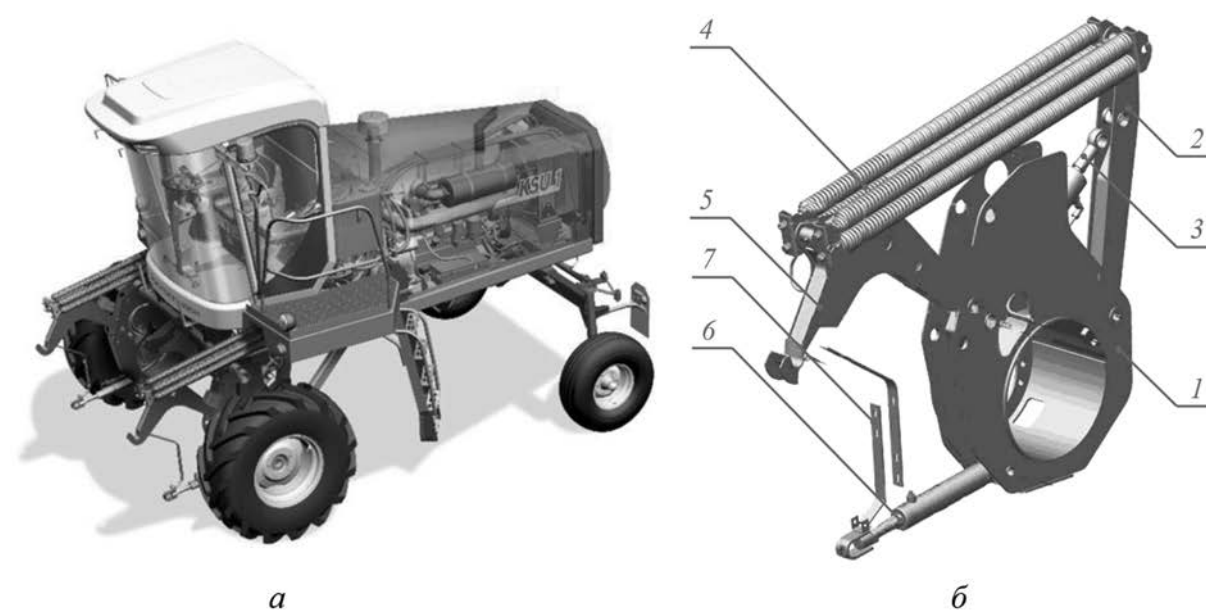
Общий вид самоходной уборочной косилки (а) и механизма агрегатирования (б): 1 – рама; 2, 5 – двуплечий поворотный рычаг; 3 – гидроцилиндр подъема; 4 – блок уравнивающих пружин с телескопической тягой; 6 – гидроцилиндр угла атаки нижней тяги; 7 – растяжка
